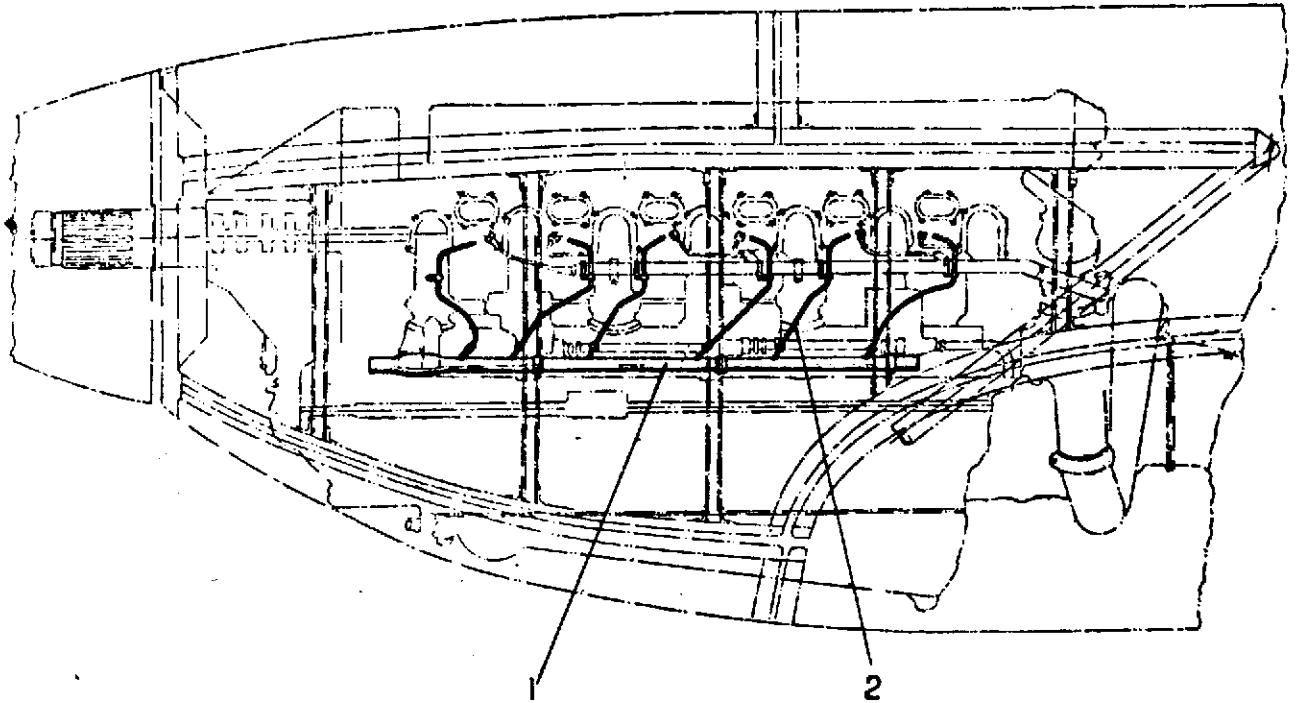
СХЕМА КОЛЛЕКТОРА ОБДУВА
